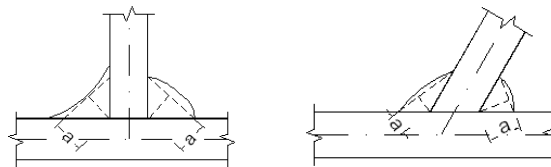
Espesor de garganta en cordones de soldadura en ángulo
